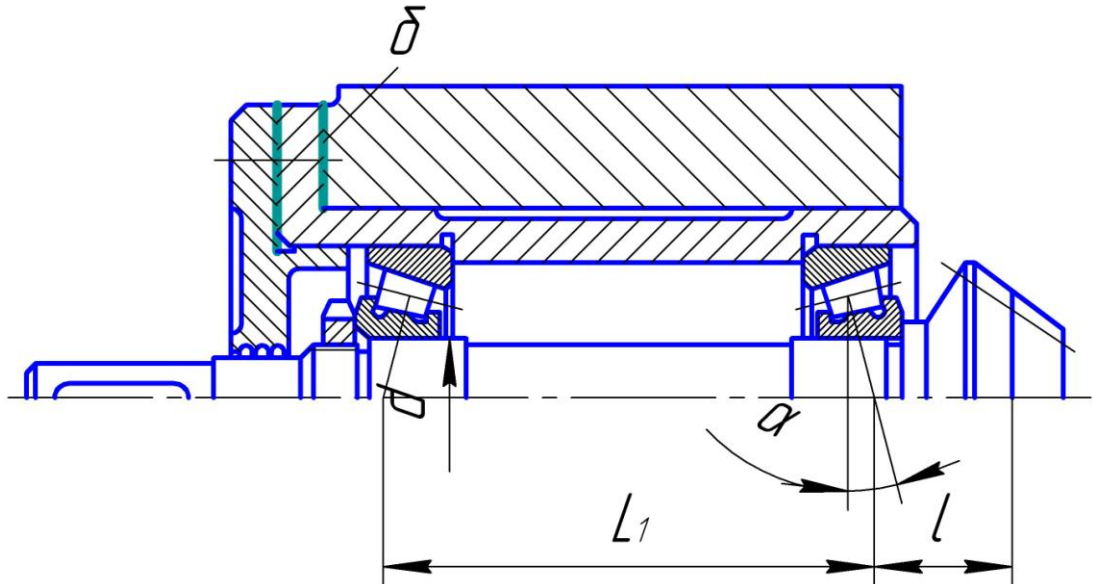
Схеми установки вала на конічних роликопідшипниках, поставлених в розтяжку
